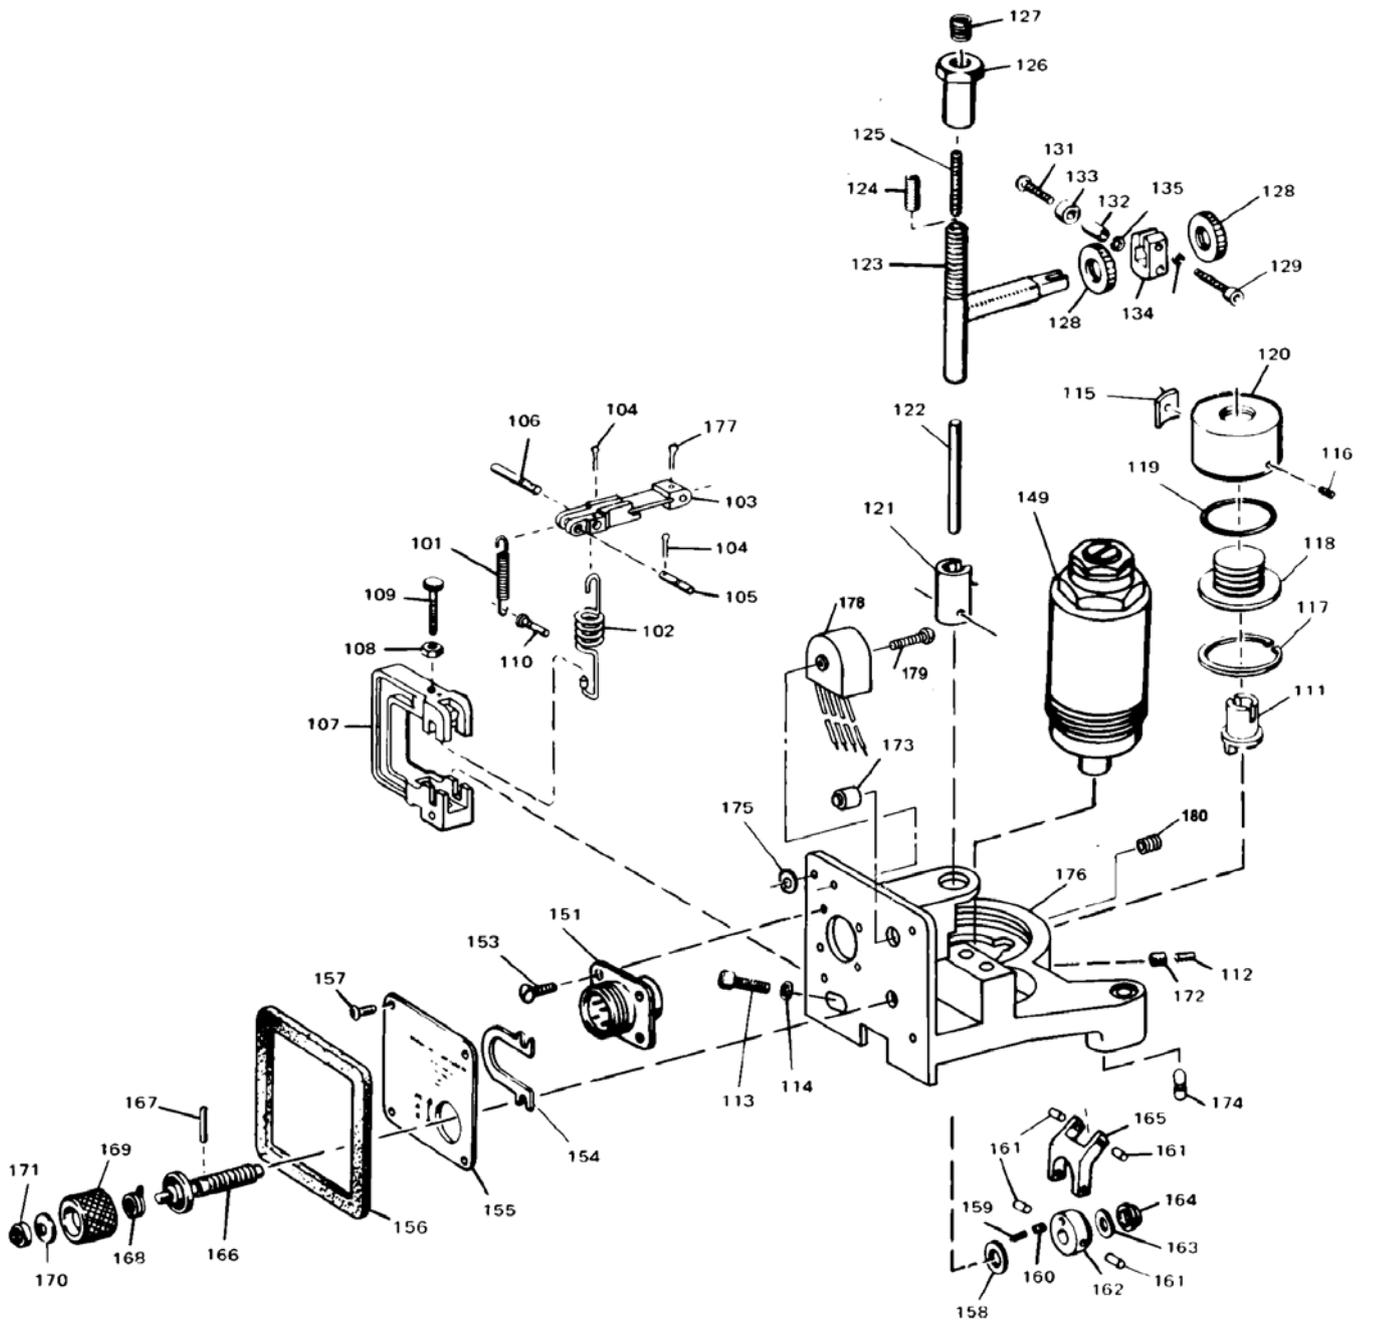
Покомпонентный чертеж ресивера PGA в сборе
